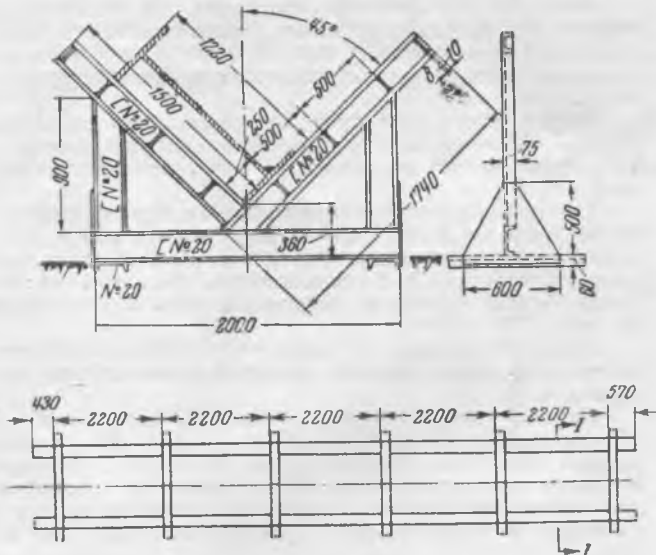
Кондуктор для сварки колонн и балок электросварочным автоматом.]
